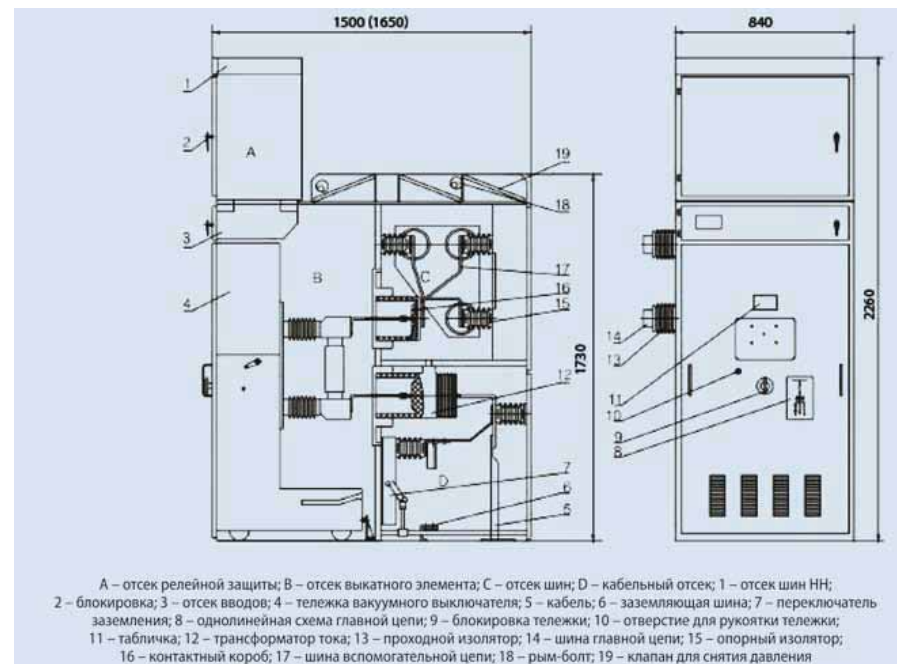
Габаритные размеры и вид РУ KYN1-12Z
